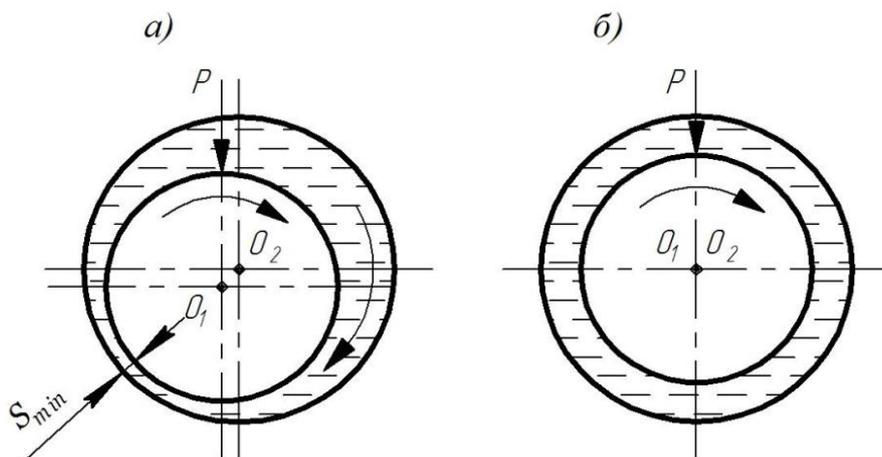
Схема формирования масляного клина в подшипнике скольжения коленчатого вала: O_1 – центр шейки коленчатого вала; O_2 – центр подшипника
